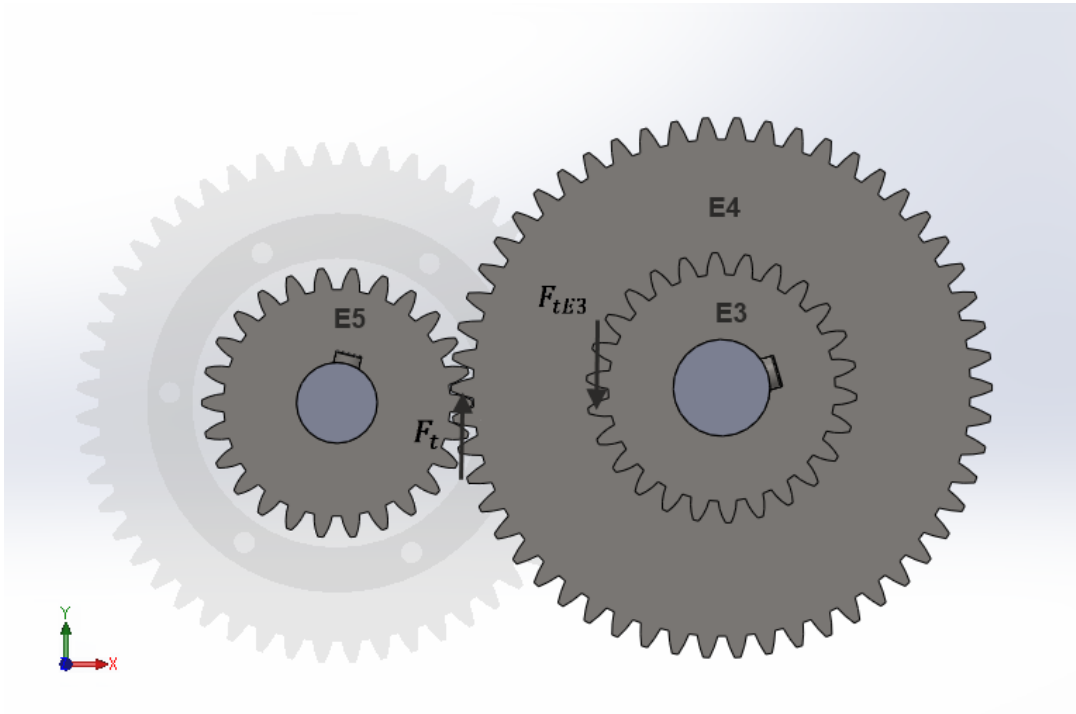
Fuerzas actuantes en el engranaje E3, engranaje E4 y engranaje E5. Fuente: Elaboración propia.
